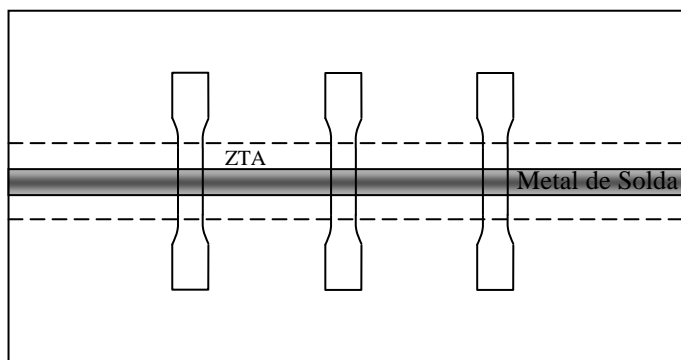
Modo de retirada dos corpos-de-prova de tração em cada junta soldada.
